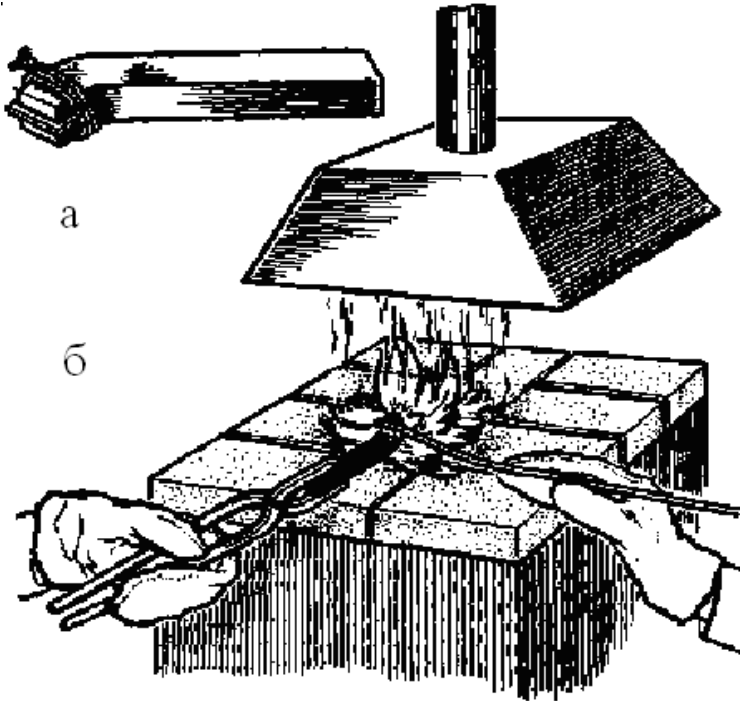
Паяння середньоплавким припоєм твердосплавної пластини до токарного різця
